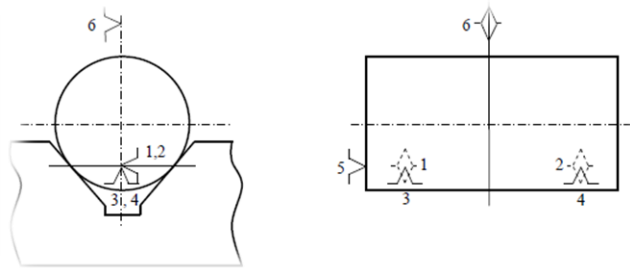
Установка цилиндрической заготовки в призмах опорных
